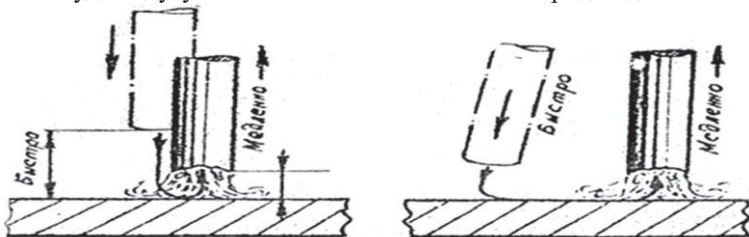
а, б. Схема зажигания сварочной дуги.
